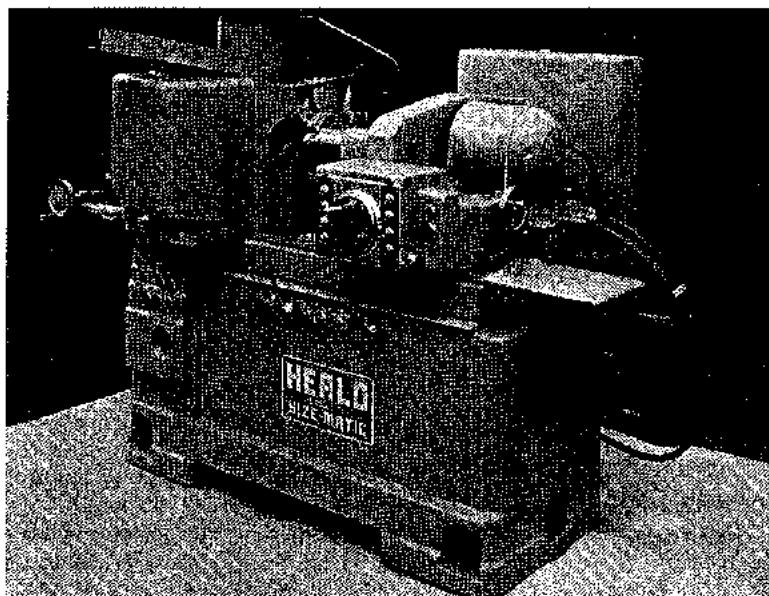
Rectificadora de interiores sin puntos (Heald Machine Co.)
